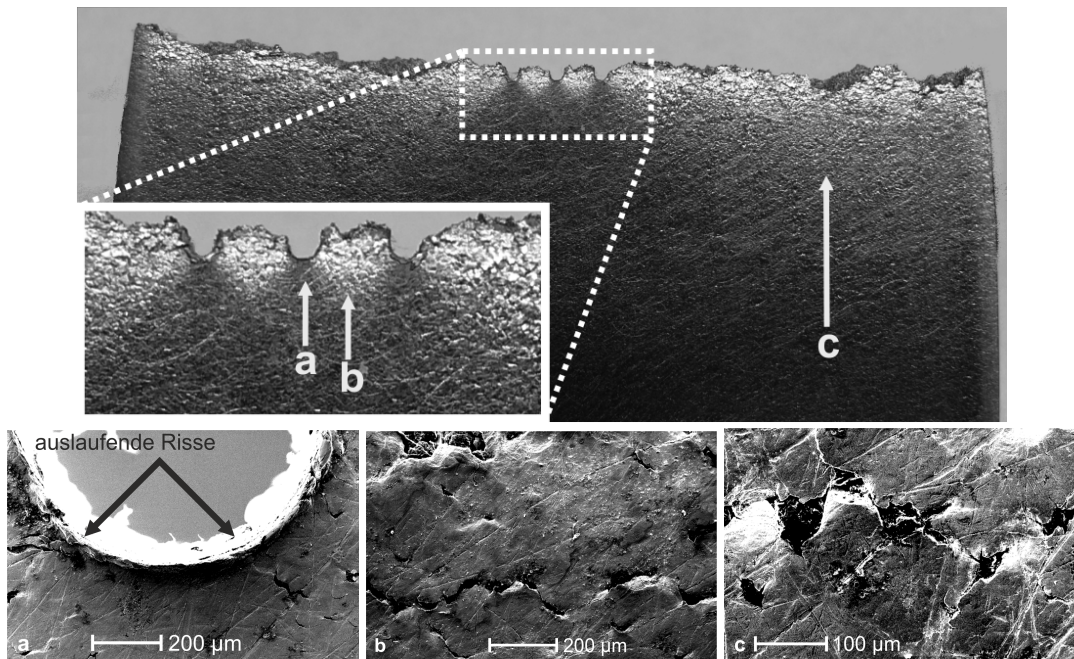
Oberfläche der Geometrieprobe G1 mit 1,0 mm Lochdurchmesser. a) auslaufende Risse nahe des Kerbgrunds, b) + c) Mikrorisse senkrecht zur Belastungsrichtung.
